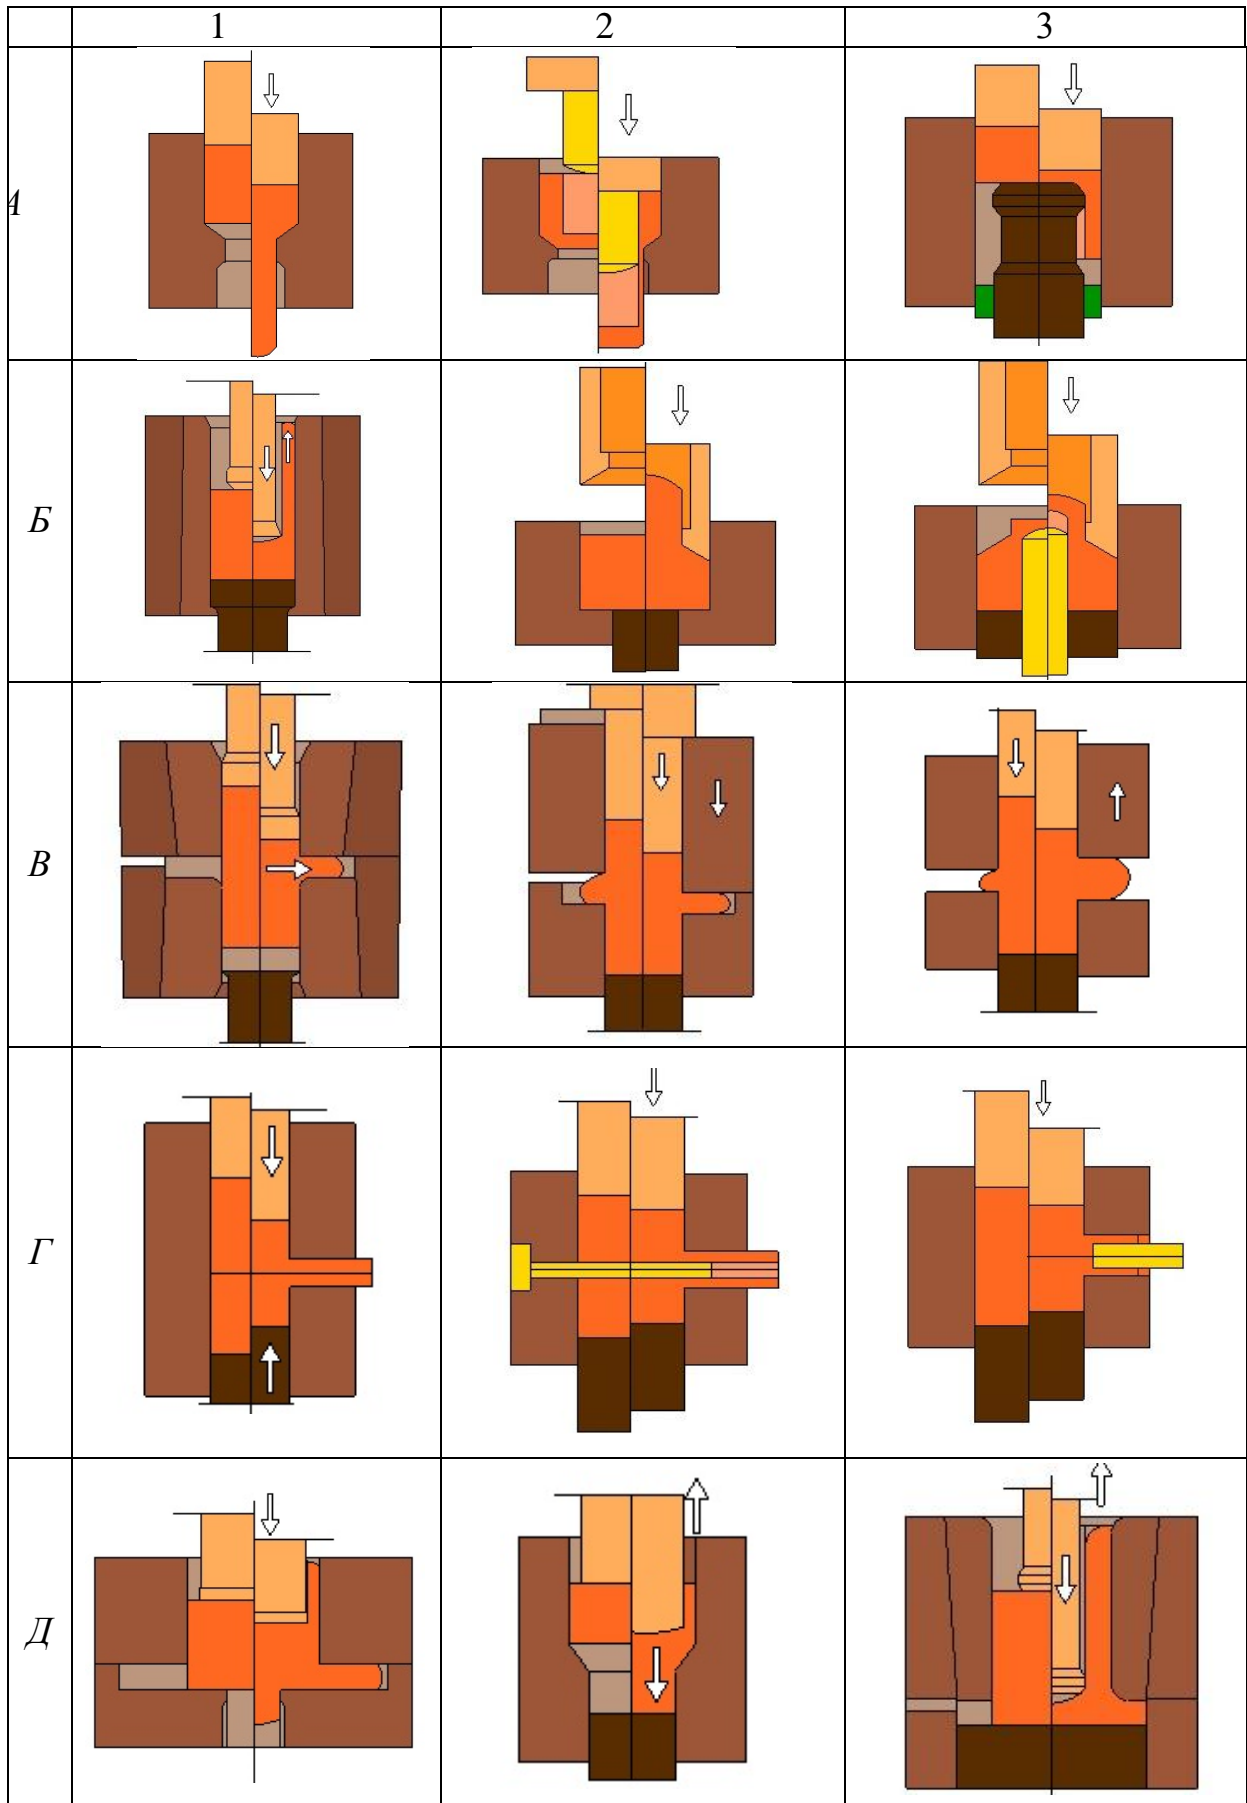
Застосування способів холодного видавлювання для виготовлення деталей різного типу
